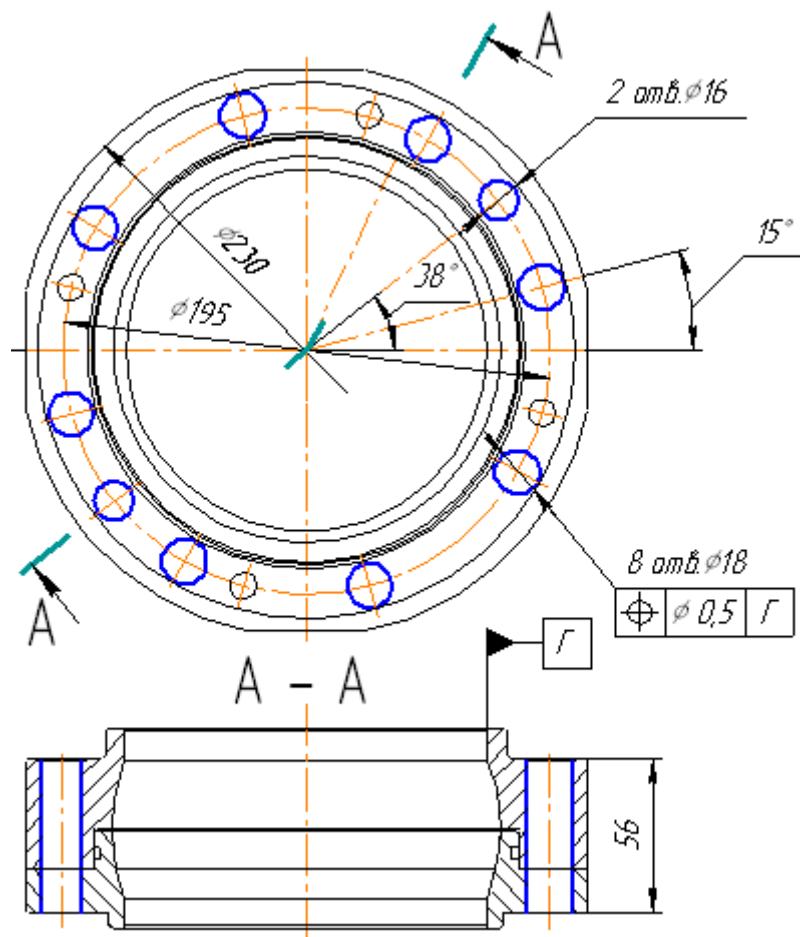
Ескіз обробки заготовки на операції 040
